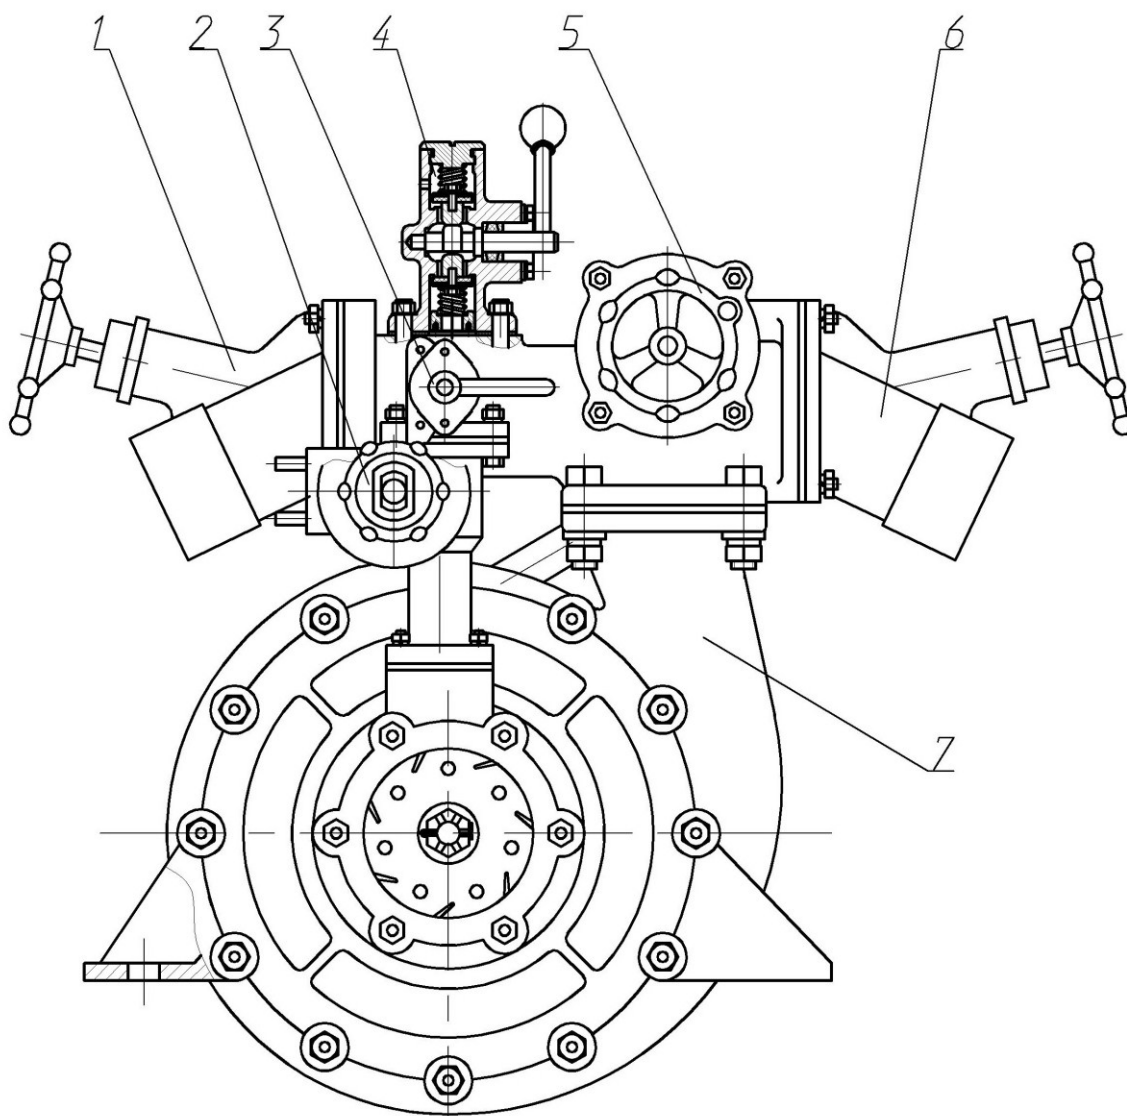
Пожарный насос ПН-40УВ (общий вид): 1 - левая напорная задвижка; 2- маховичок дозатора пеносмесителя ПС-5; 3 – кран пеносмесителя; 4 – вакуумный клапан; 5 – задвижка в цистерну; 6 – правая напорная задвижка; 7 –корпус насоса.
